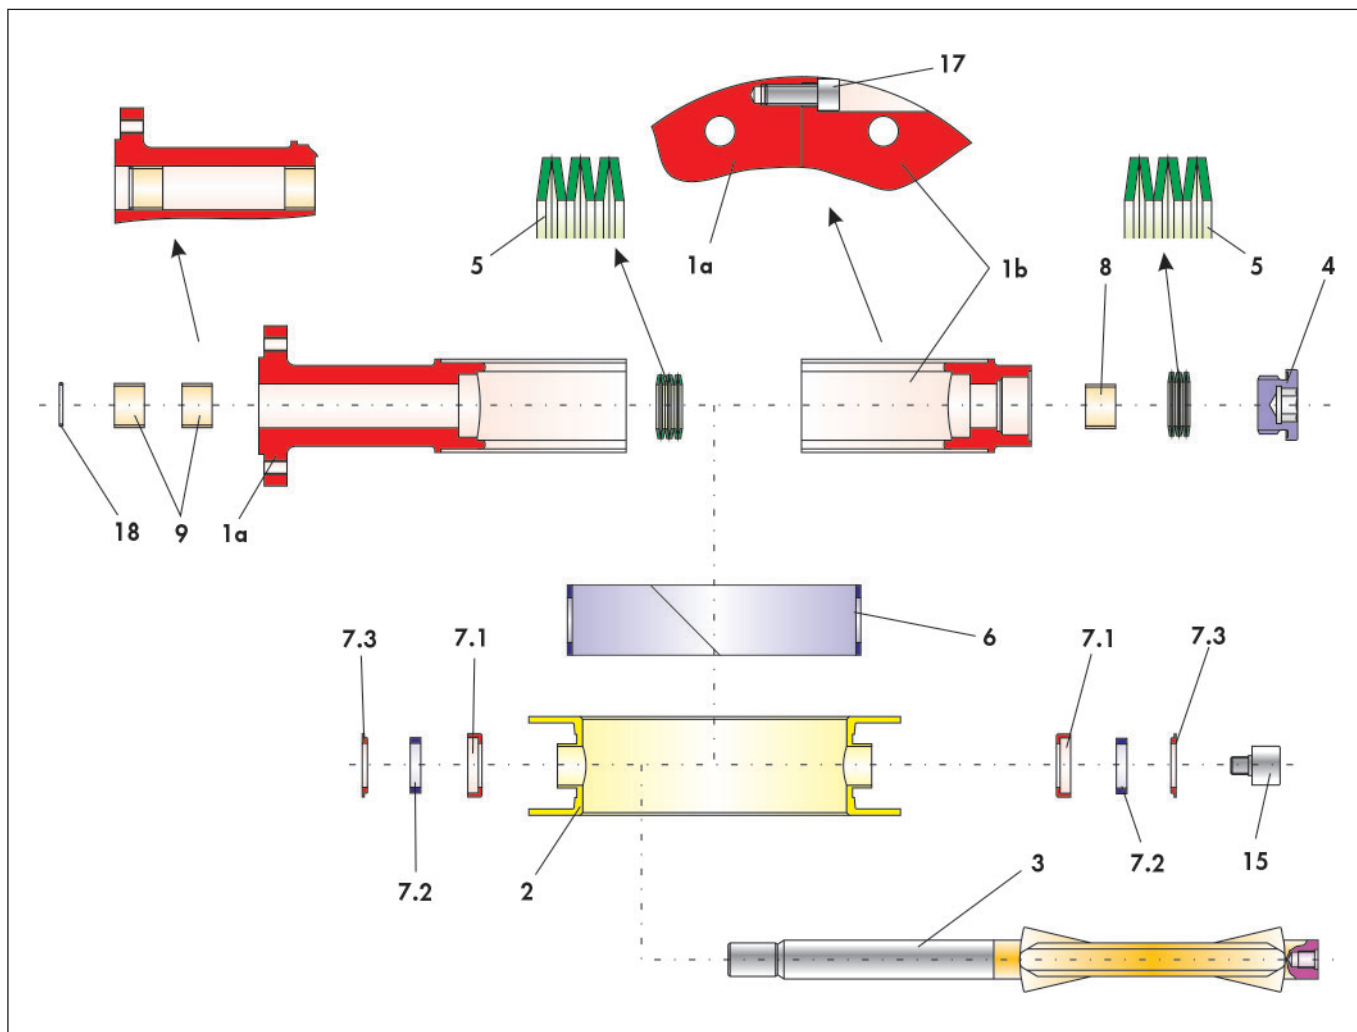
Сборочный чертеж заслонки BR 10e
